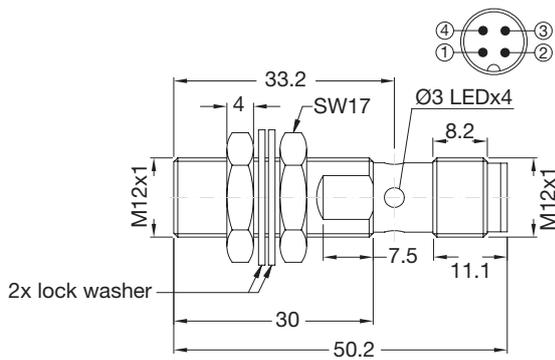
Kurze Ausführung, bündiger Einbau, Steckversion
